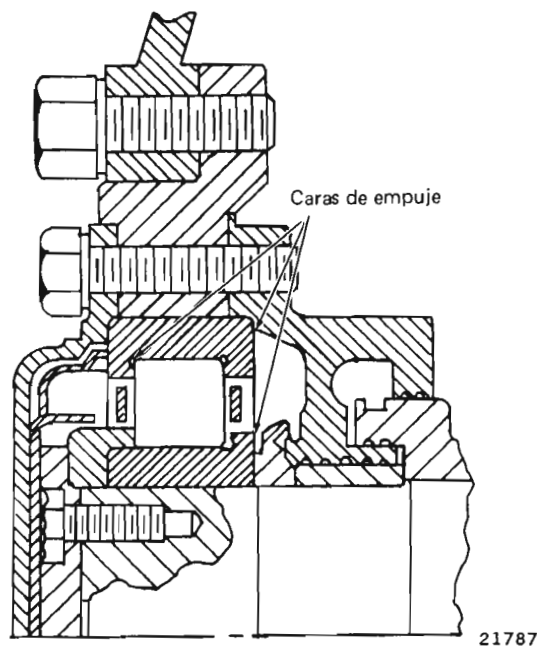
Corte del cojinete del extremo del conmutador de un motor de tracción
